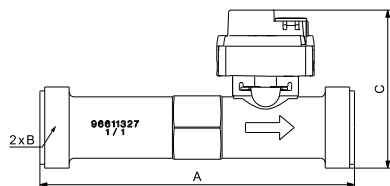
Abmessungen des Sensors VFS 5-100 l/min (ohne Adapter)
